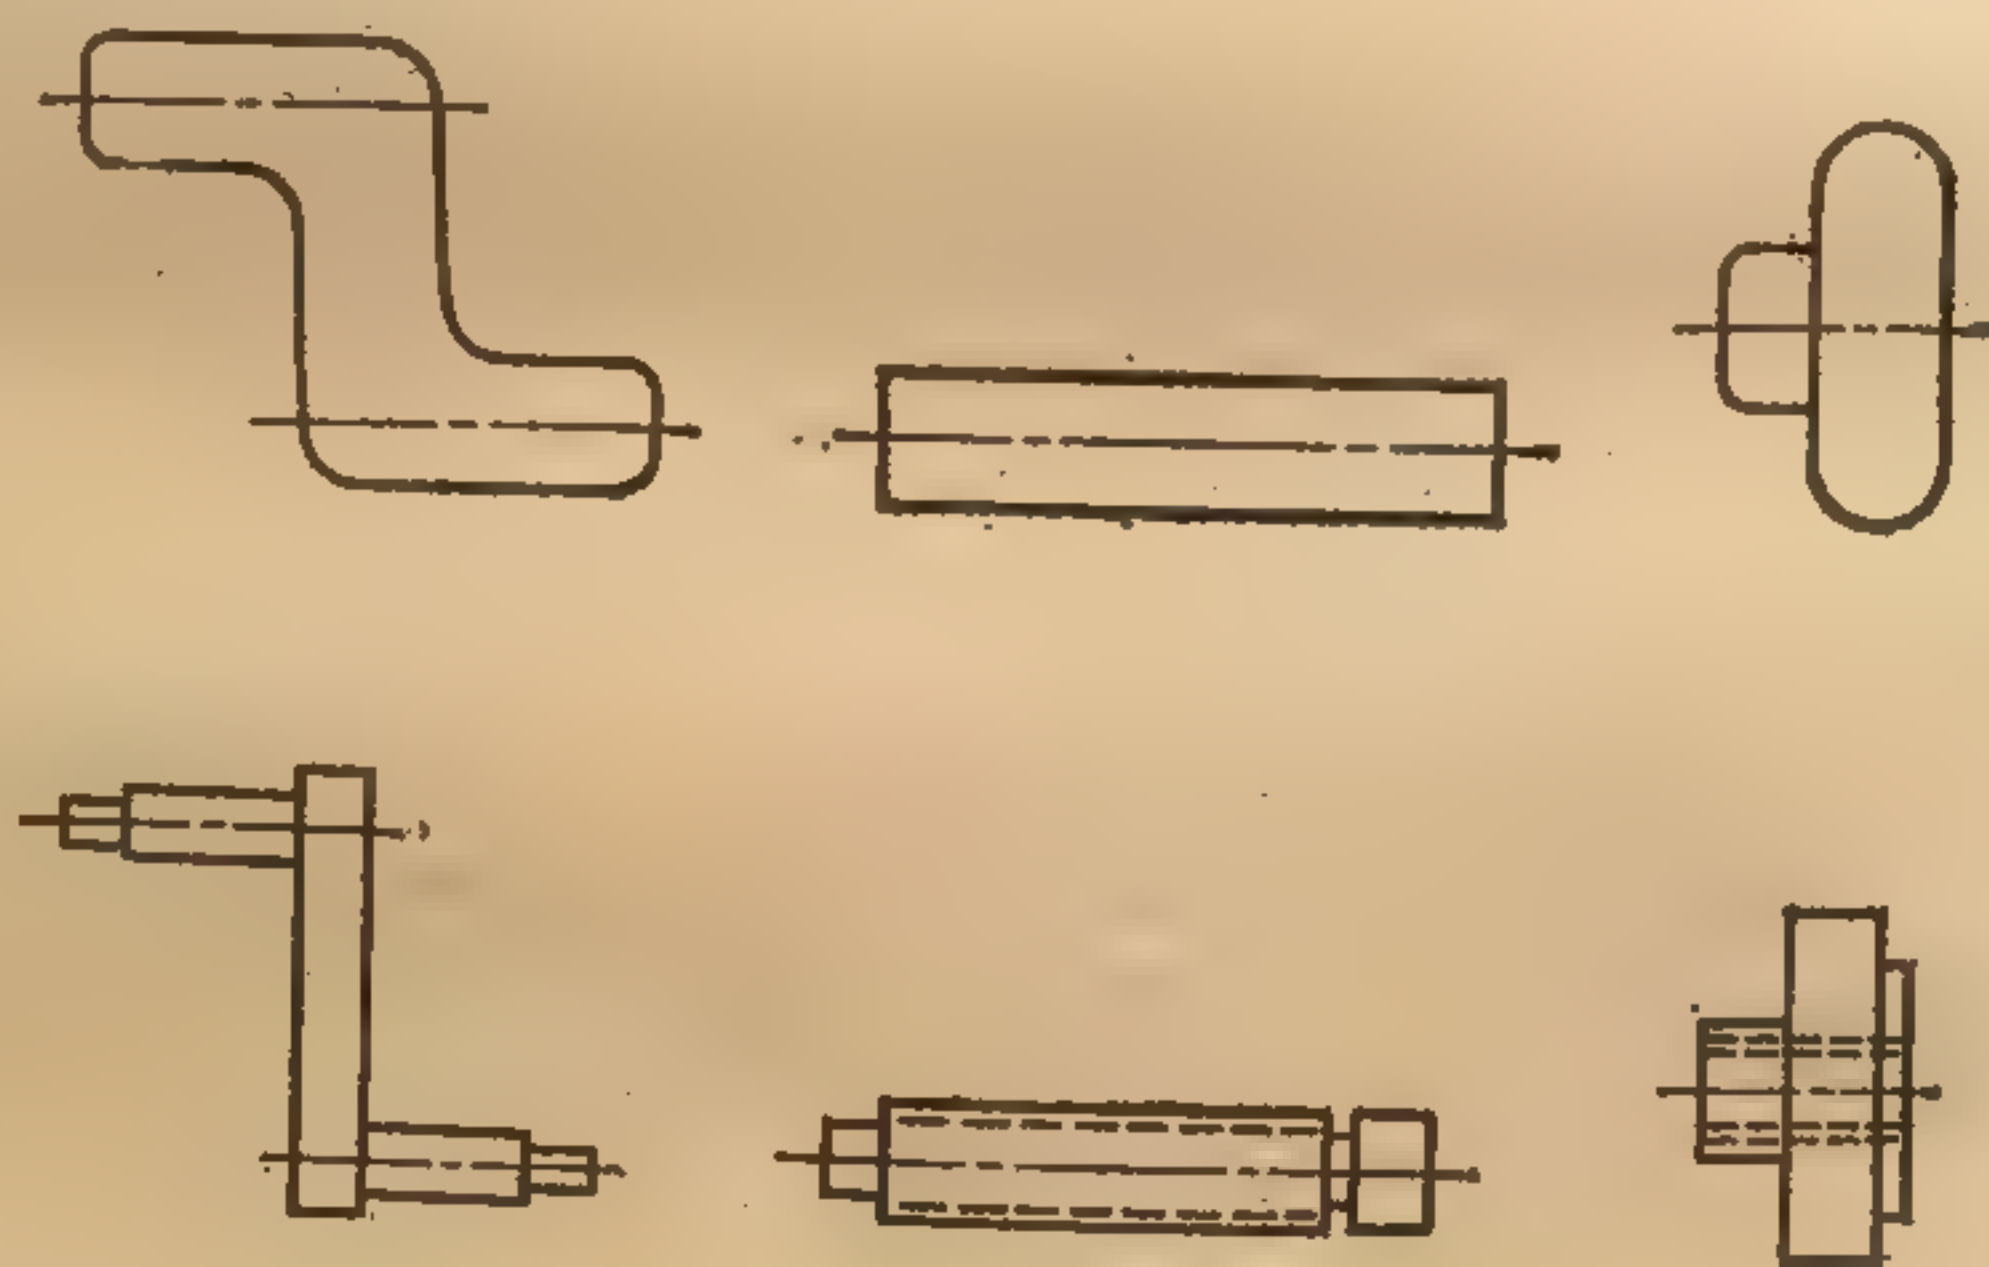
Чертежи деталей ■ карточке-задании по выбору установочных и измерительных баз
